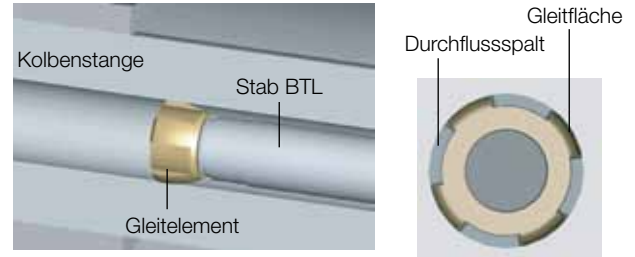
Detailsicht und Draufsicht Gleitelement
